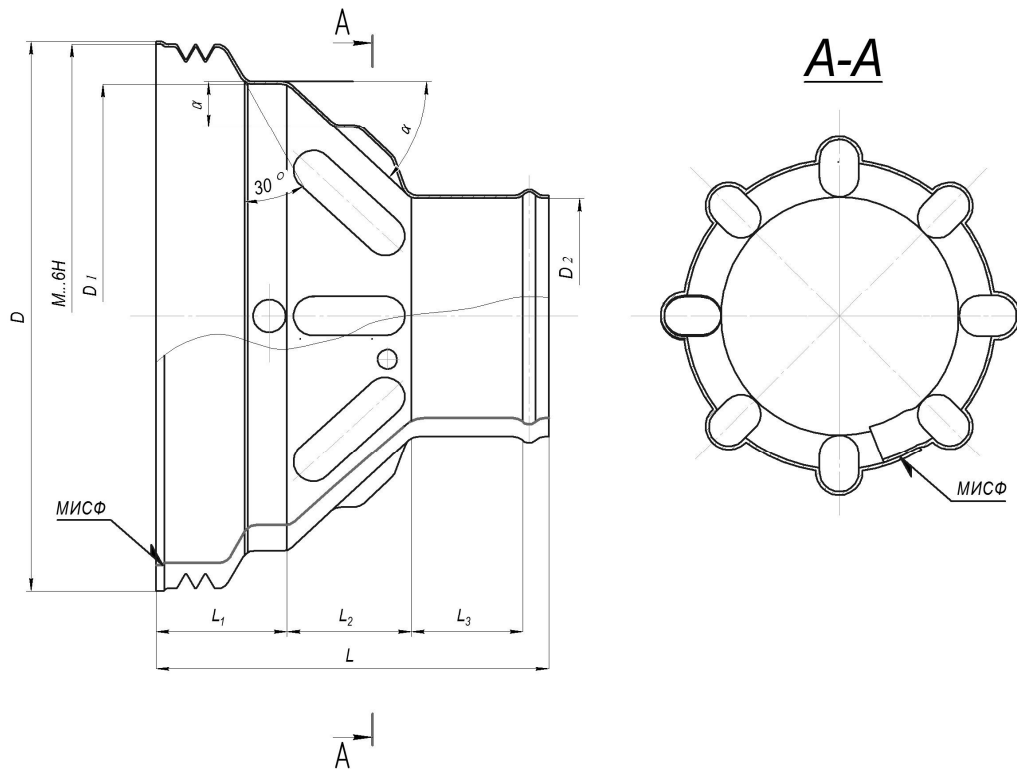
Эскиз экранирующего штампосварного корпуса
